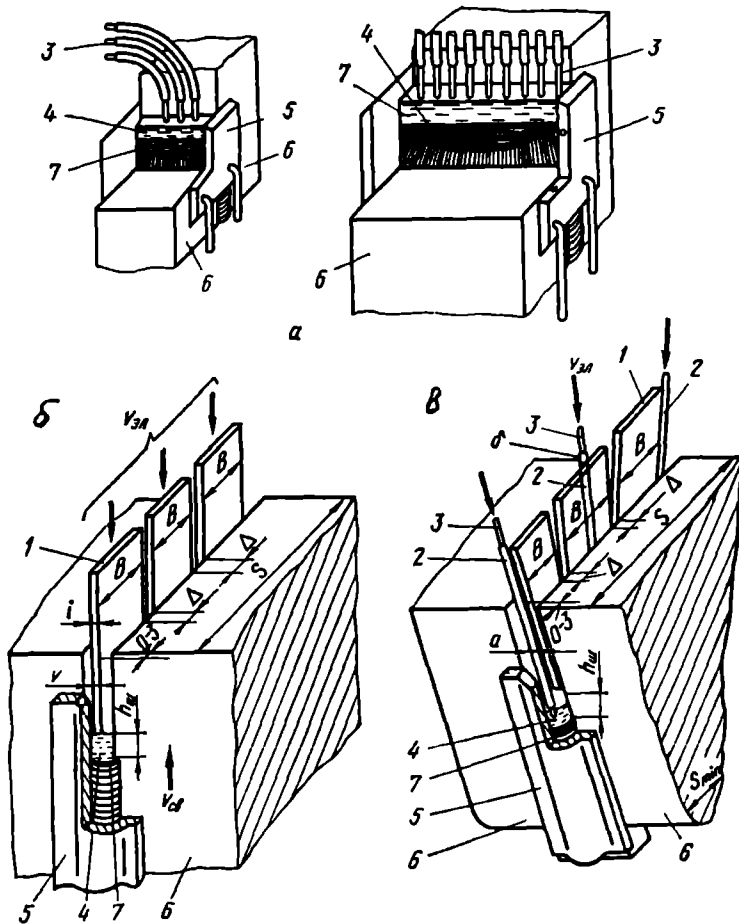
Схема процесса электрошлаковой сварки:
